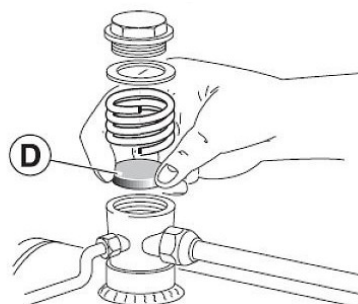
Élément d'étanchéité dans le clapet anti-retour
